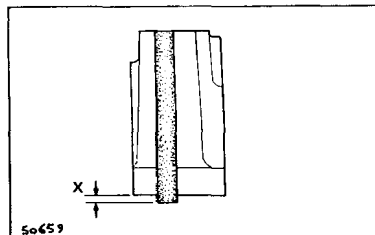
Размещение уплотнения в крышке коренного подшипника №1
